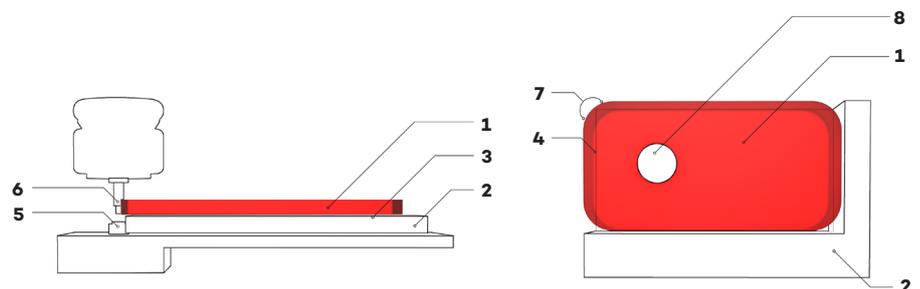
Prinzipskizze zum Kopierfräsen mit einer Oberfräse
